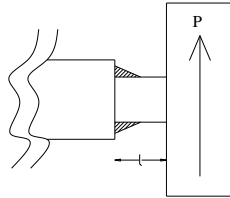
Jant takımı için kaynak geometrik şekli
